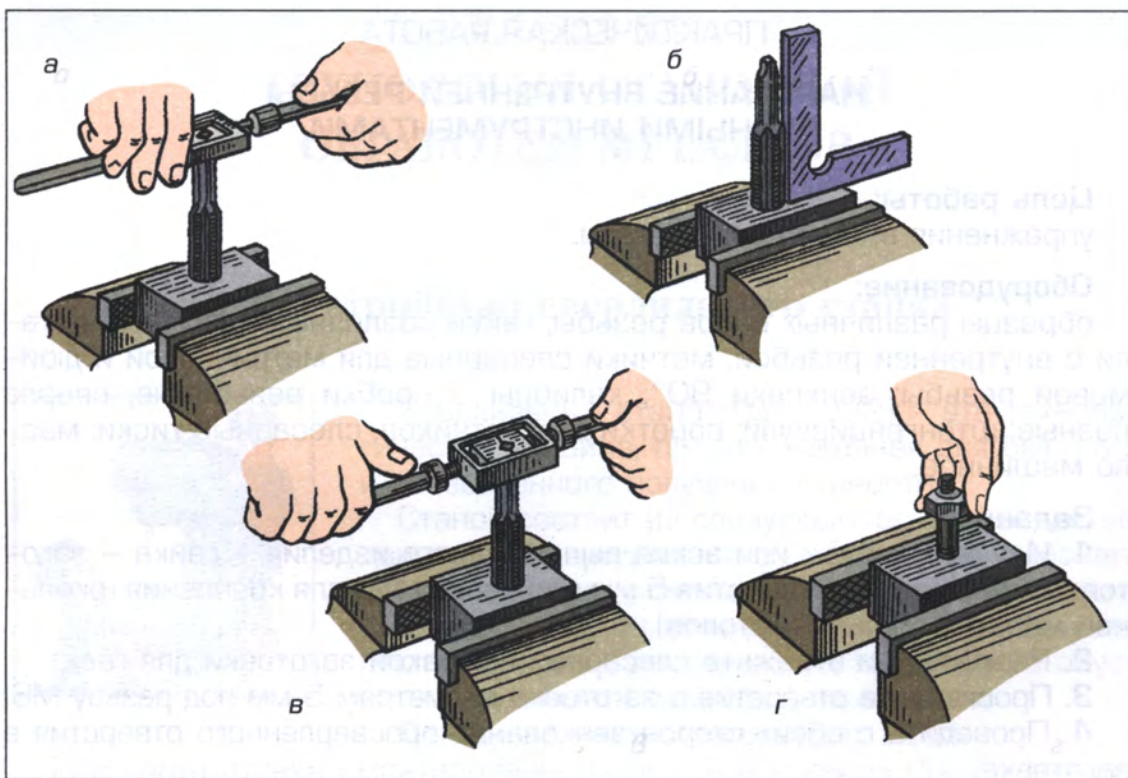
Порядок операций при нарезании резьбы метчиком: установка метчика (а), проверка перпендикулярности установки инструмента (б), нарезание резьбы (в), контроль качества (г)
